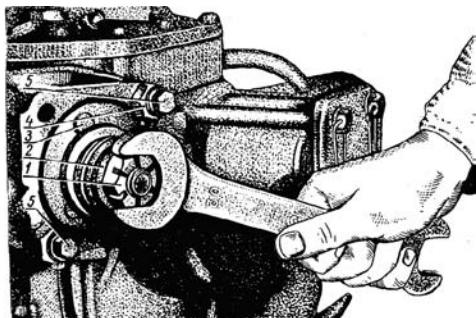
Установка распределителя и затяжка сферической гайки червяка:
